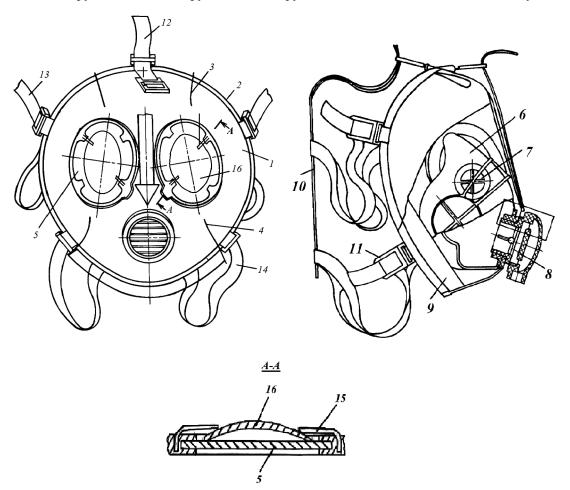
Респиратор для защиты органов зрения и дыхания работников агропромышленного комплекса от воздействия вредных веществ [7]: I — корпус маски; 2 — периметр; 3 — лобная складка; 4 — подбородочная складка; 5 — очки; 6 — подмасочник; 7 — клапан вдоха; 8 — клапан выдоха; 9 — обтюратор; 10 — наголовник; 11 — пряжка; 12—15 — зажимы; 16 — линза
